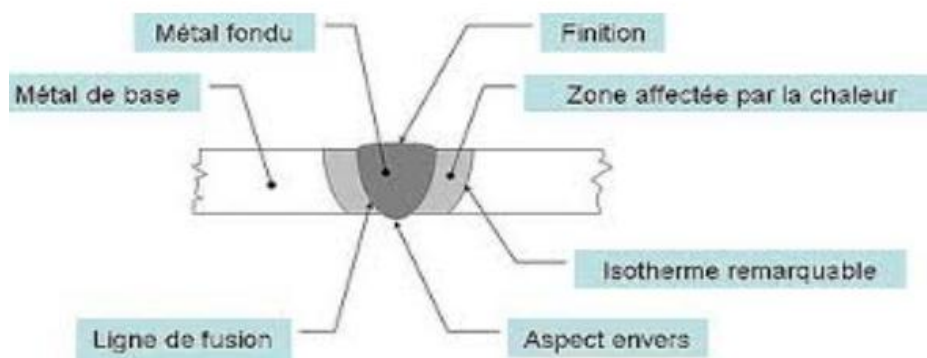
Zones principales d'un cordon de soudure par fusion.
